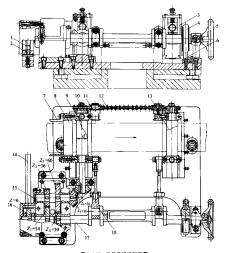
横向斜排送科装置 1一棘轮; 2、8、10一轴; 3、11一锥齿轮; 4一直齿轮; 5一平面凸轮; 6一送料辊; 7一拖板; 9—槽轮机构
